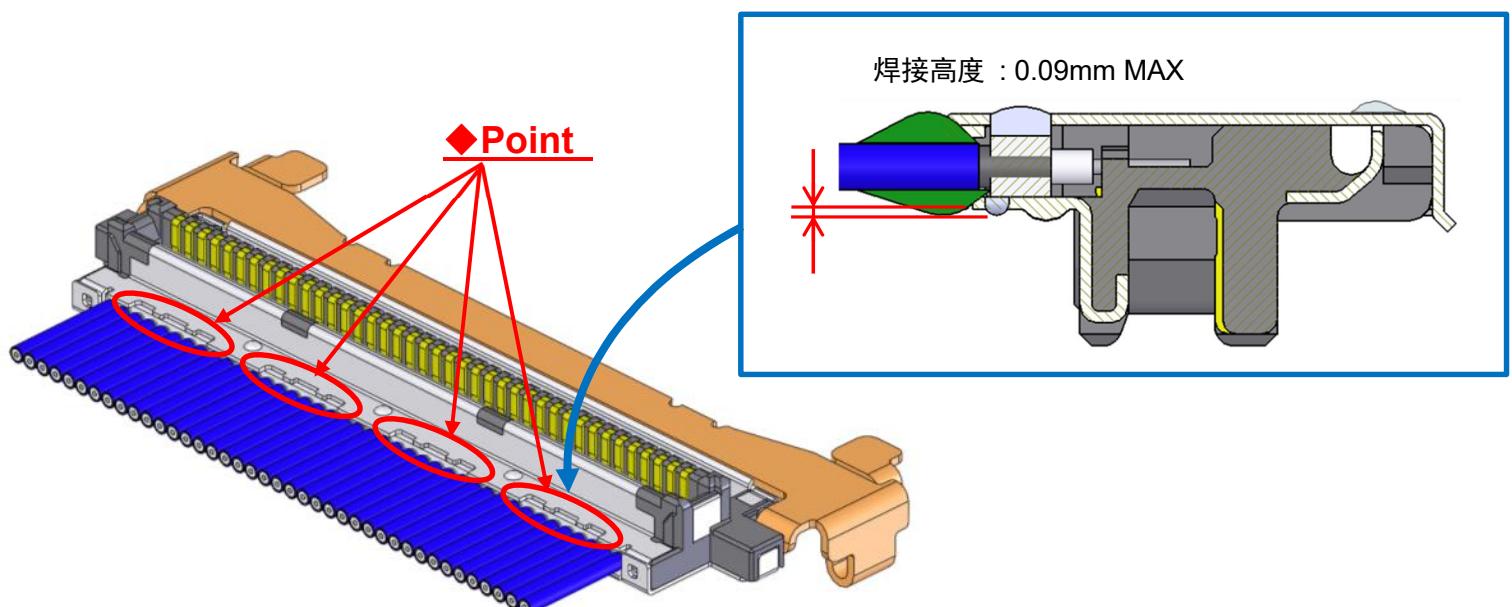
焊接 Shell-B 和 Ground Bar
